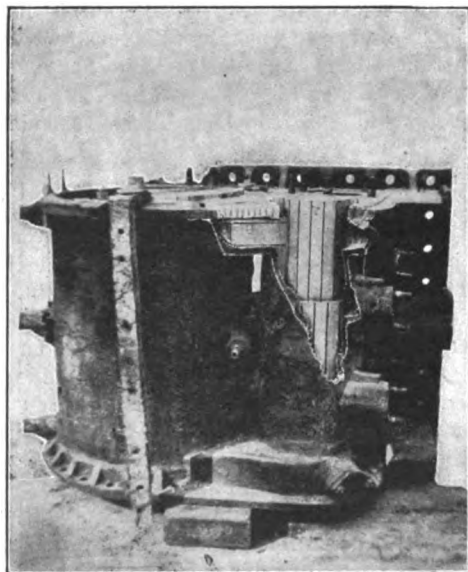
Beschädigter Lokomotivzylinder, eingeformt.
